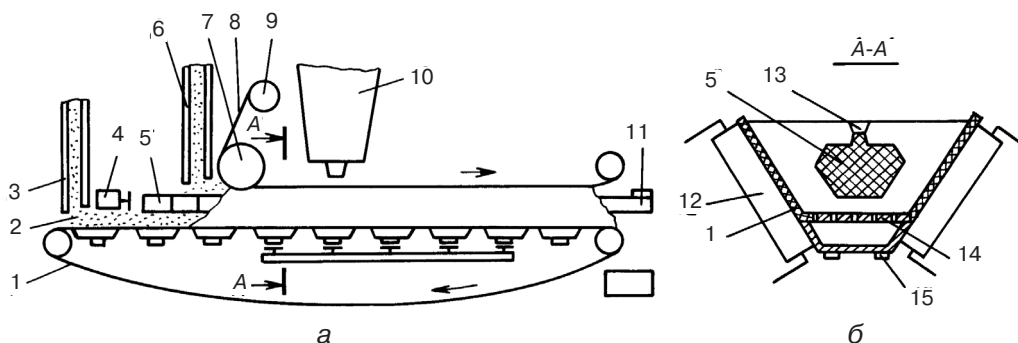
Схема установки: а – вид сбоку; б – вариант конструкции бесконечной ленты, поперечный разрез
